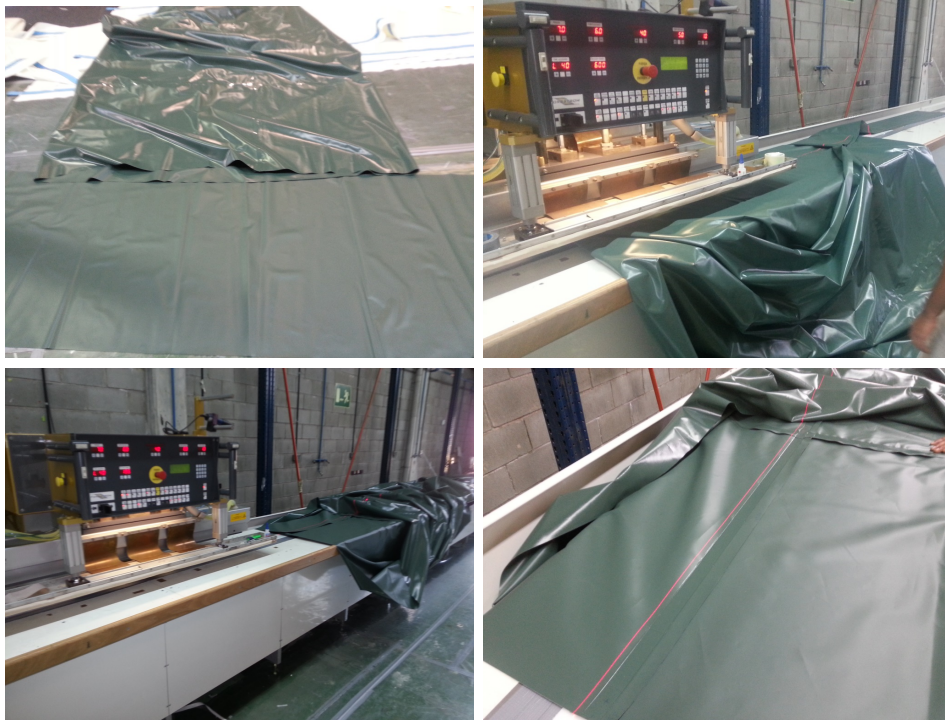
Soldadura del cuerpo central de la cámara interior del tubo hinchable
